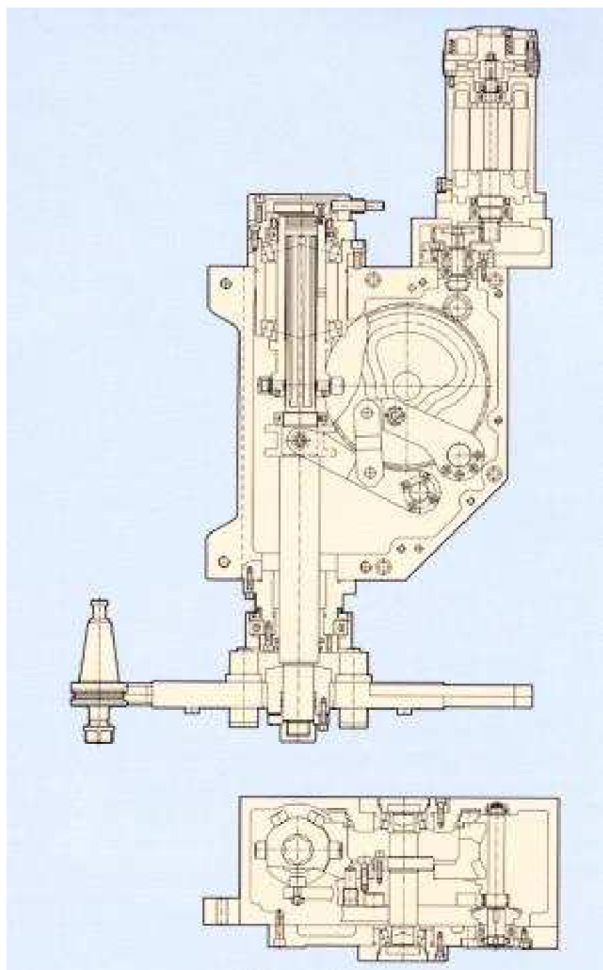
Manipulátor fy. TOS VARNSDORF [5]
